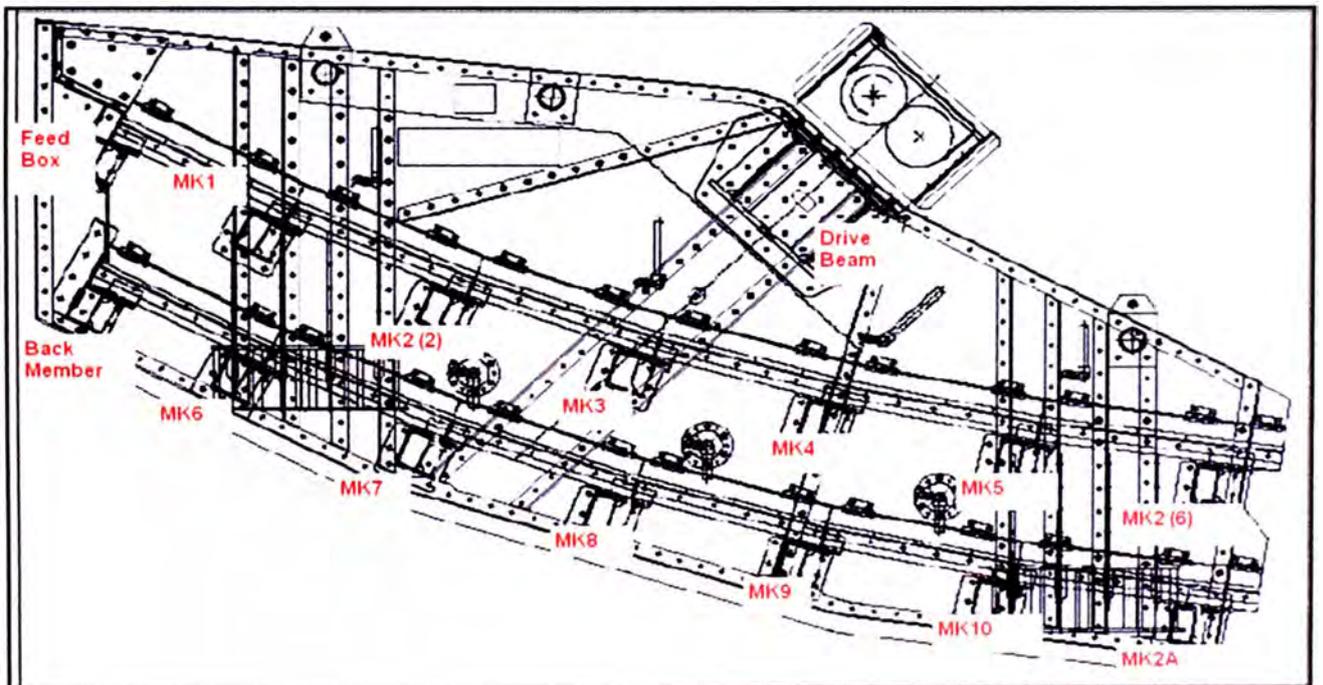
Zaranda Vibratoria Hornert, esquema estructural.
